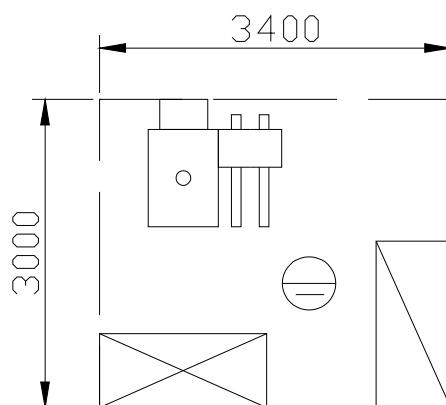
Организация рабочих мест у одношпиндеольного фрезерного станка с нижним расположением шпинделя с кареткой ФСШ, $F = 10,2 \text{ м}^2$
